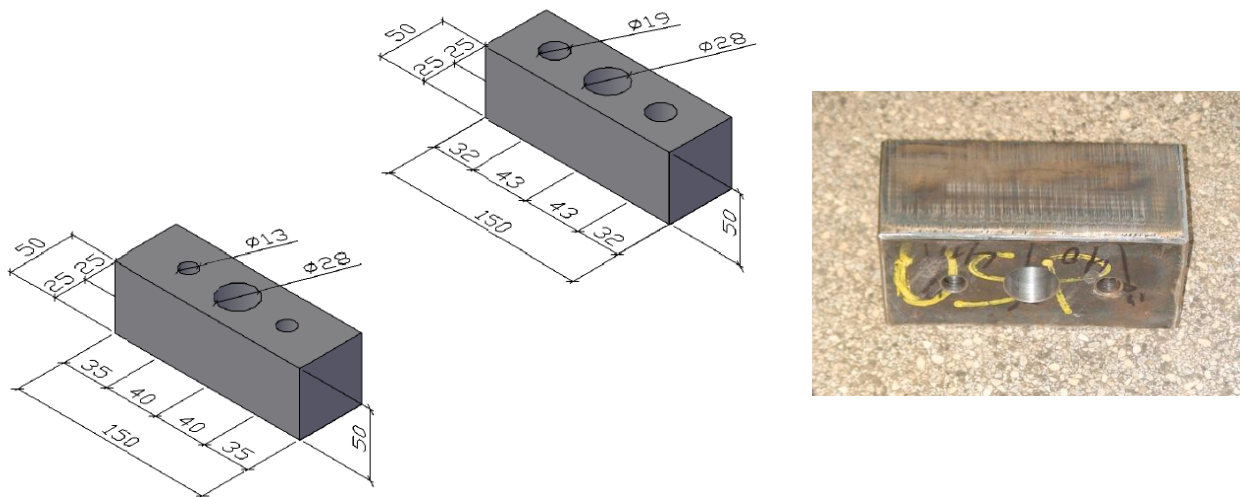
Peça para fixação das barras a serem ensaiadas (dimensões em mm)
